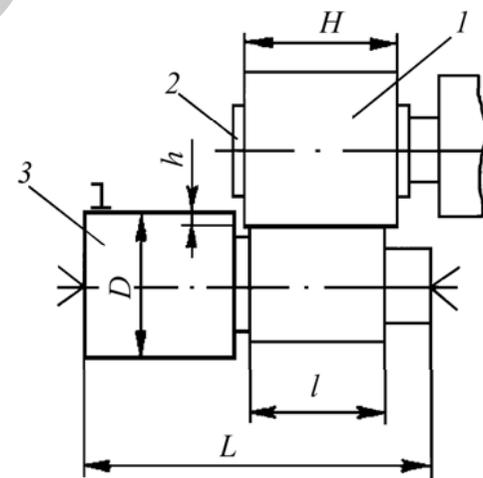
Схема установки детали на шлифовальном станке
